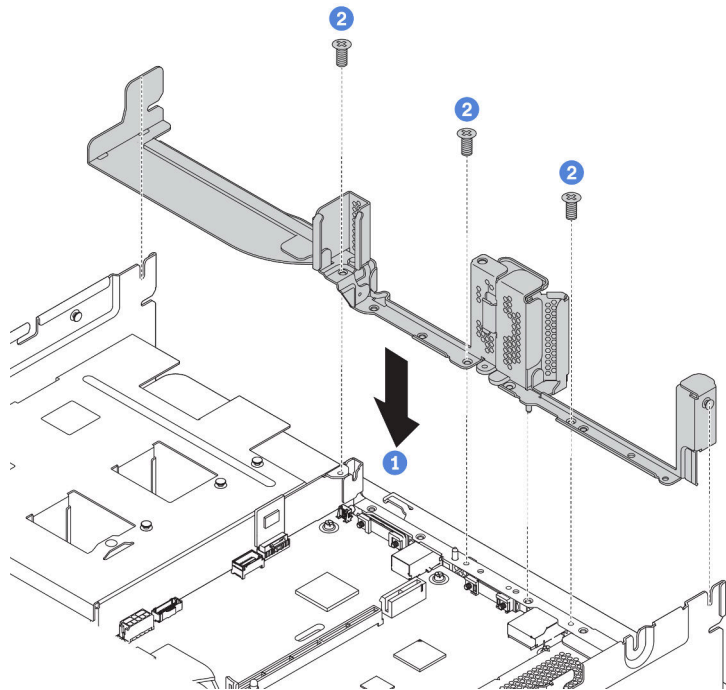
Installation du support mural arrière pour le boîtier d'unités arrière 2,5 pouces
